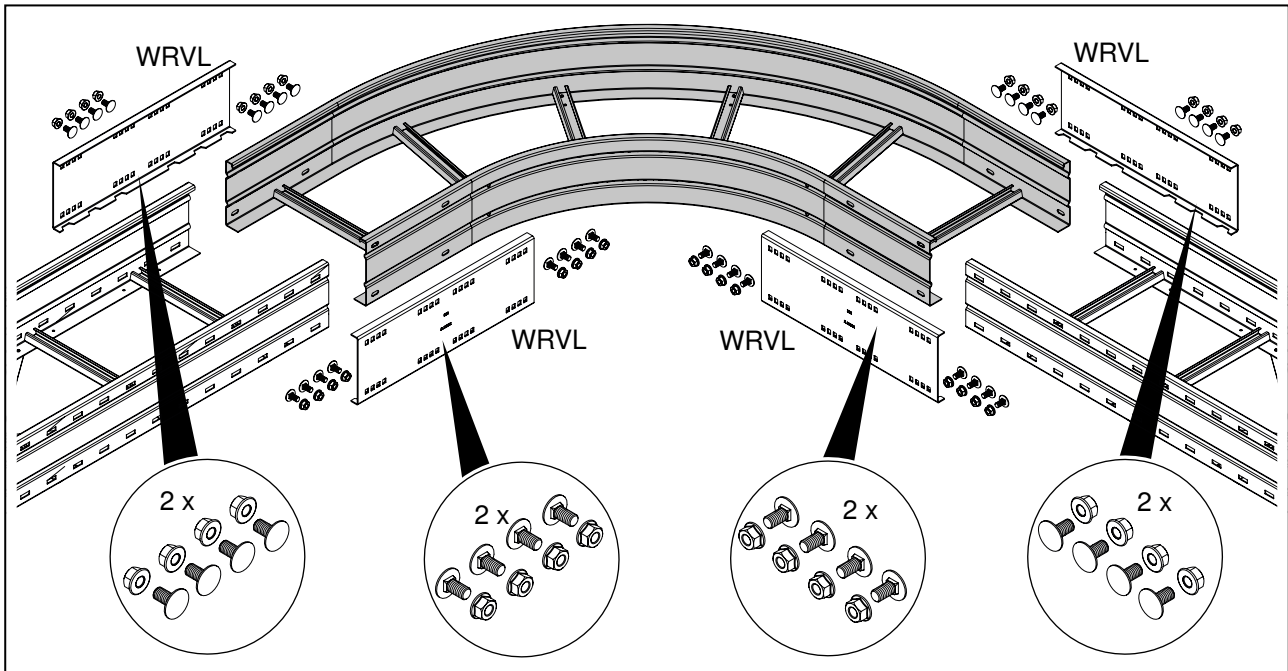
Bauteile für Montage Bogen 90° Seitenhöhe 160 mm
